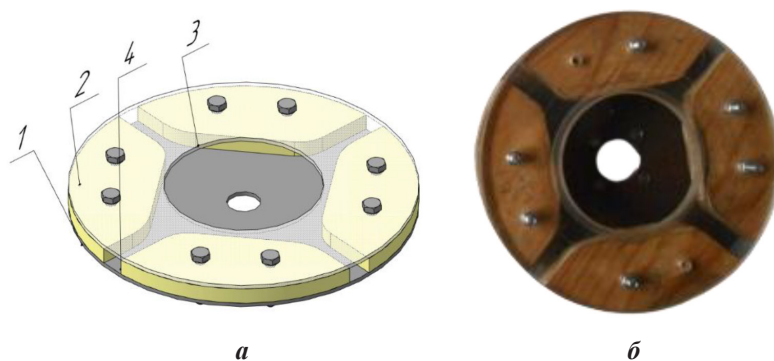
Схема (а) та загальний вигляд (б) робочого колеса: 1 – нижній диск; 2 – верхній диск; 3 – завантажувальний отвір; 4 – профільний канал
